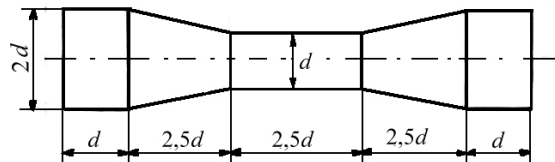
Циліндричний зразок із крихкого матеріалу для випробувань на розтяг
